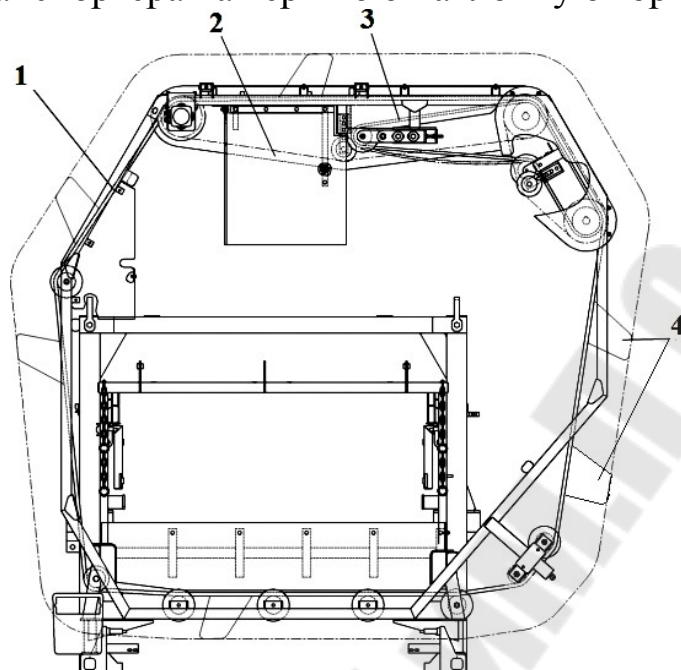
Транспортер подъемный: 1 – транспортер; 2 – передача цепная; 3 – транспортер сопроводительный; 4 – ковши
